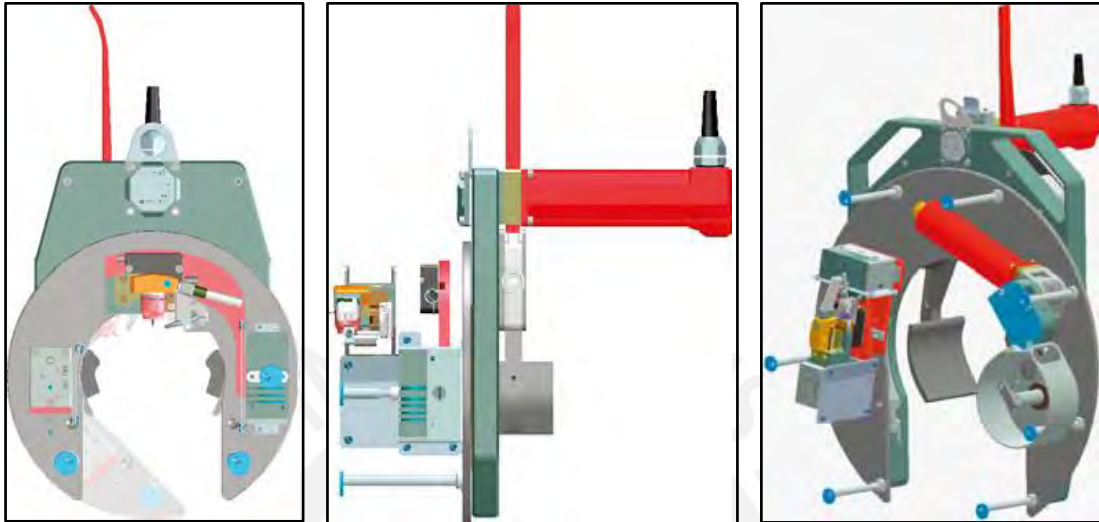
Vistas del cabezal de soldadura MU IV 128 de la gama POLYSUDE.
